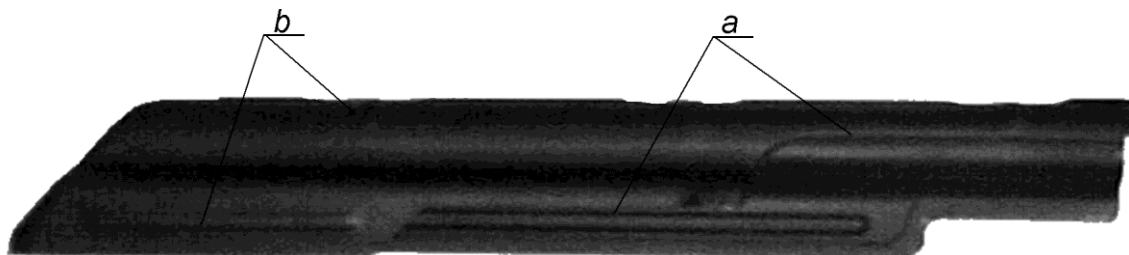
Położenie części mechanizmu spustowego w stanie zabezpieczonym
